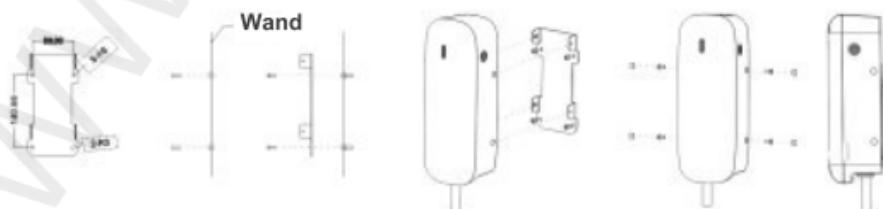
Installationsverfahren für die Wandmontage der Ladestation Modus C
